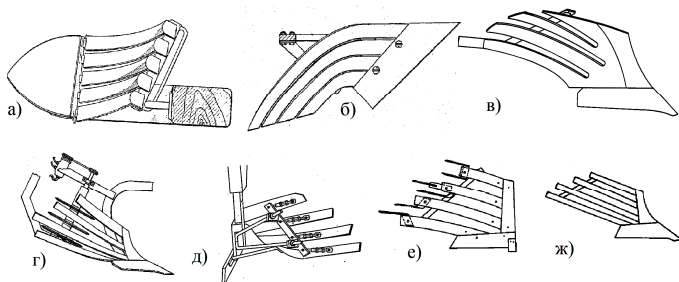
Корпуса плуга с пластинчатыми отвалами
